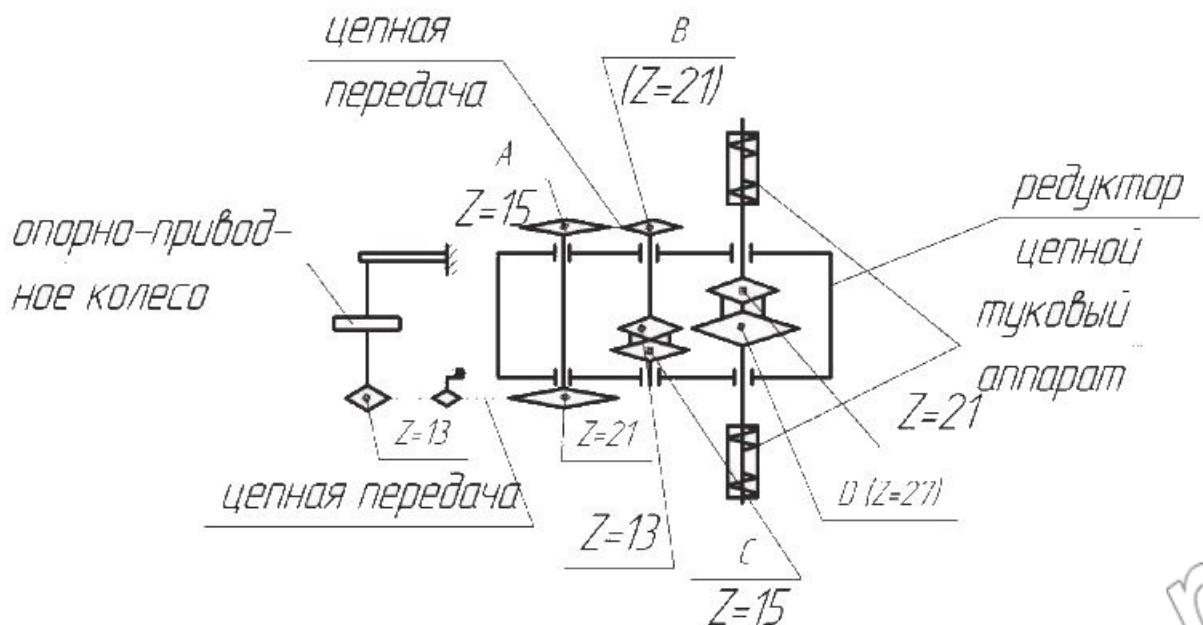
Кинематическая схема привода туковысевающих аппаратов
